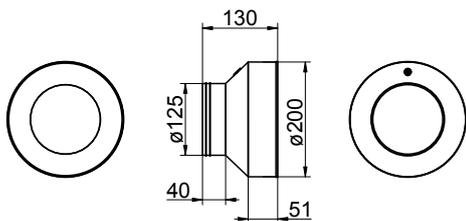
Dimensions de raccord de transition DN125 (dimensions en mm)
